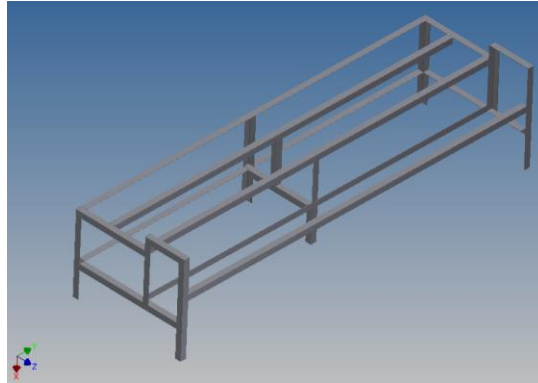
Estructura de la máquina diseñada en CAD Inventor Profesional
